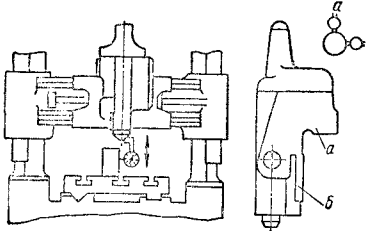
Отсчитывающий механизм координатно-расточного станка.
